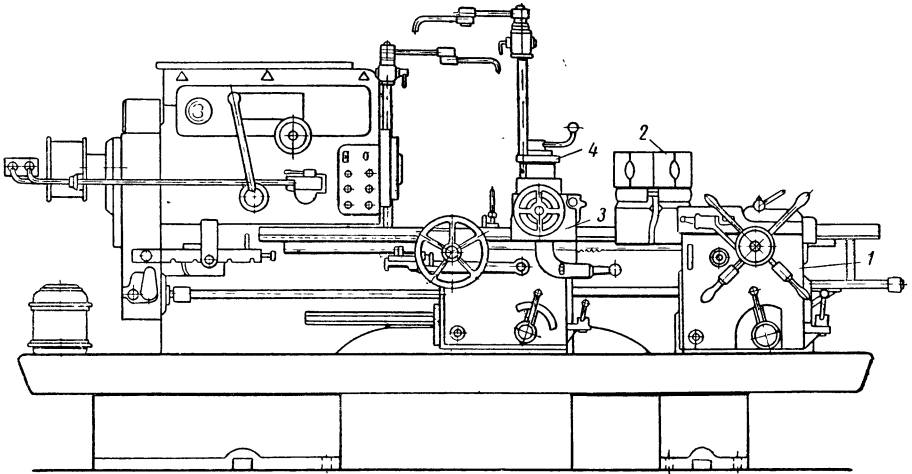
Общий вид токарно-винторезного станка модель 1620.
